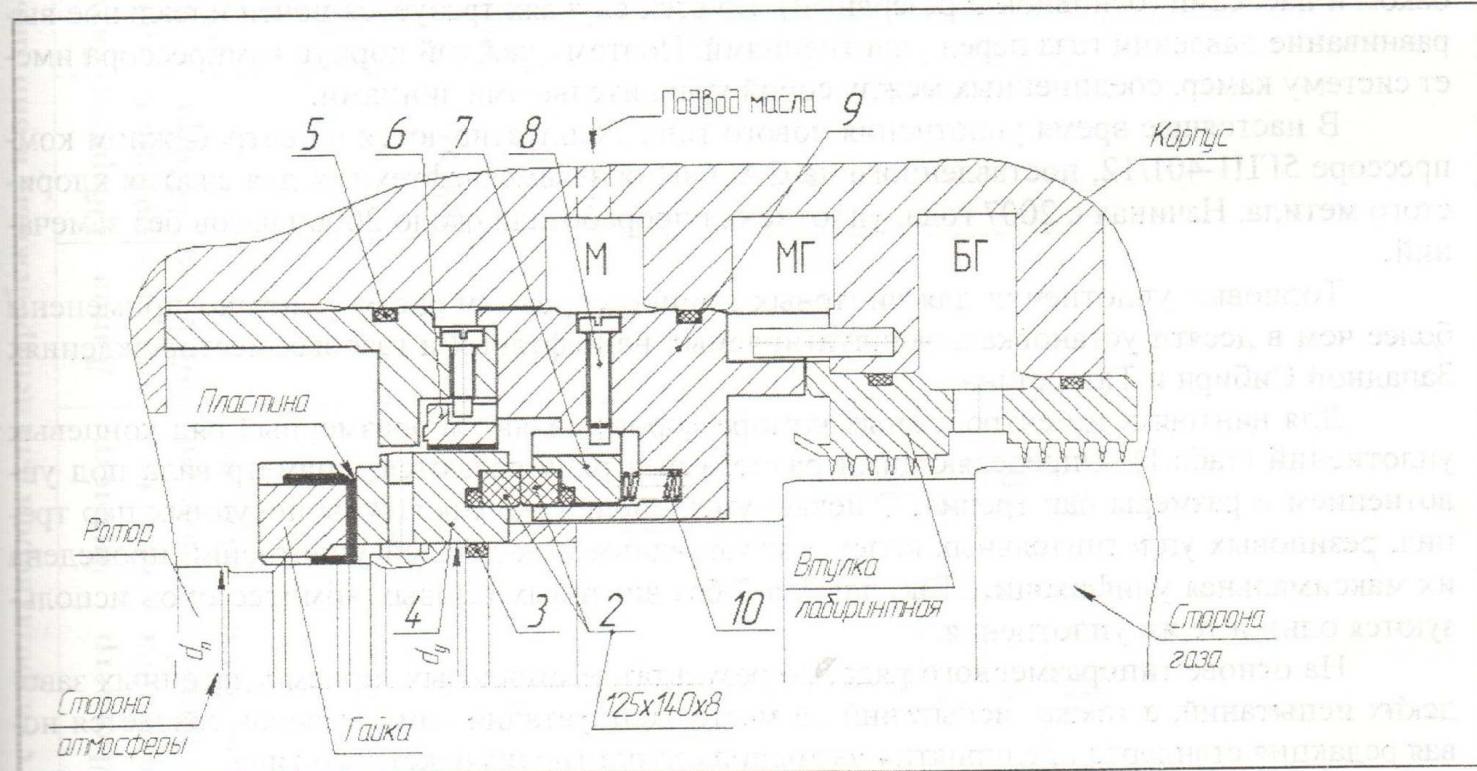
Торцовое уплотнение пакетного типа для промышленных центробежных компрессоров: 3,5 – кольцо резиновое; 2 - кольцо уплотнительное (пара трения); 4 - втулка; 6 - кольцо расходное; 7 - кольцо нажимное; 8 - винт; 9 - корпус; 10 - пружина; камеры: М- подвод масла; МГ- «масло-газ»; БГ- буферный газ.
